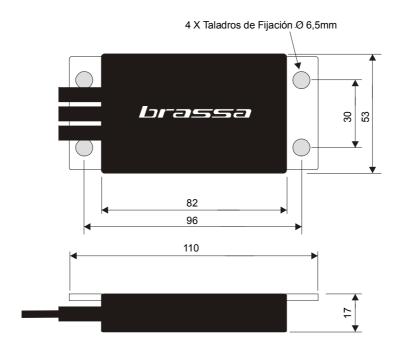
Dimensiones de la Unidad de Control CSPS-A
